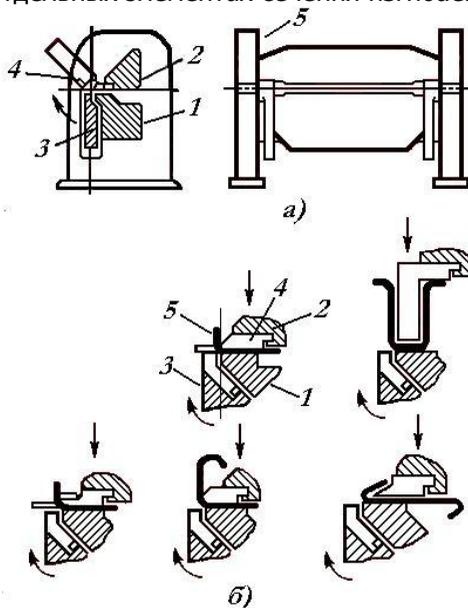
Схемы гибки в листогибочных машинах с поворотной гибочной балкой: а – схема машины; б – схема гибки различных деталей: 1 – стол; 2 – прижимная траверса; 3 – поворотная балка; 4 – шаблон; 5 – стойка; 6 – заготовка.
